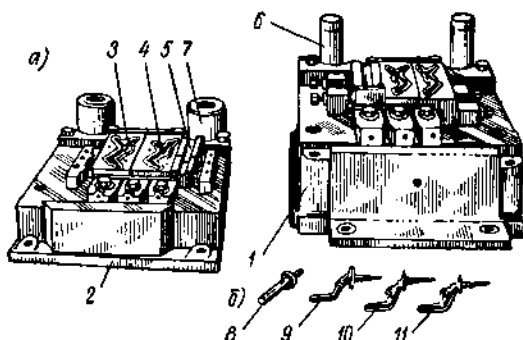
Общий вид штампа (а — верхняя половина; б — нижняя) для штамповки поковки кривошипа и технологические переходы:
